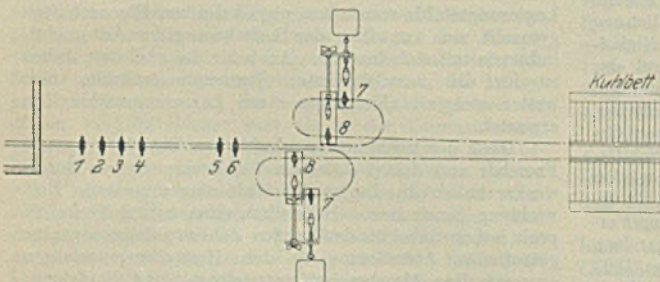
Fertigwalzen in acht Stichen. Zwei Walzstäbe.
